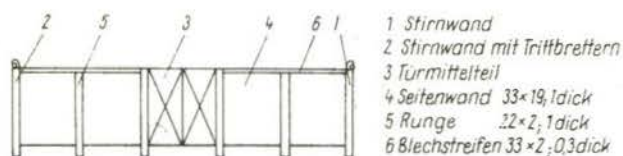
Skizze Oberteil für den Om-Wagen „Breslau“, geschweißte Ausführung
